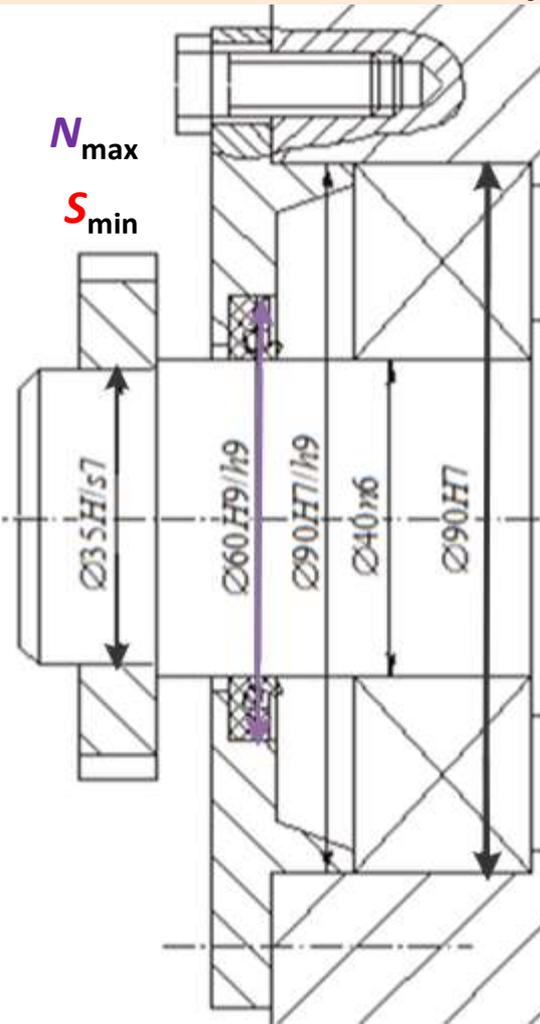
Посадки в отверстие корпуса, на вале и с крышкой с манжетой в металл.оболочке
